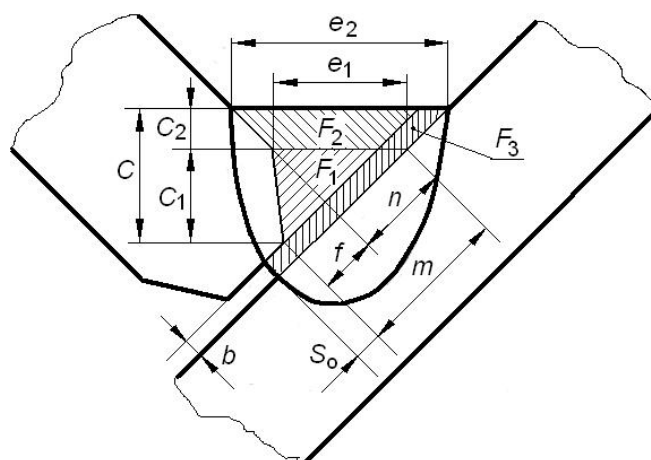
Поперечное сечение наплавленного металла при сварке углового шва с разделкой кромок
